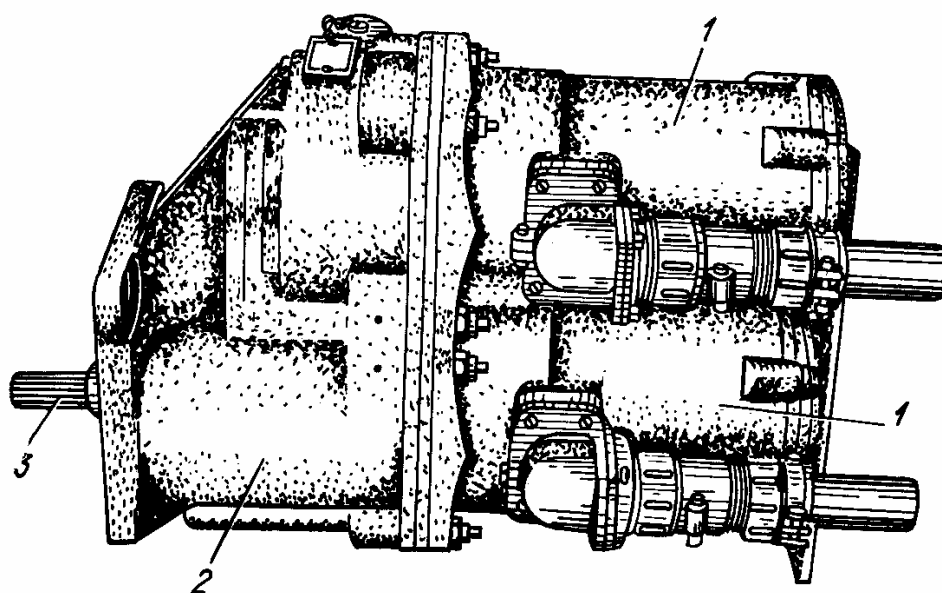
Электромеханизм ЭПВ-8П: 1—электродвигатели АДС-600Т; 2—корпус редуктора; 3—вал
